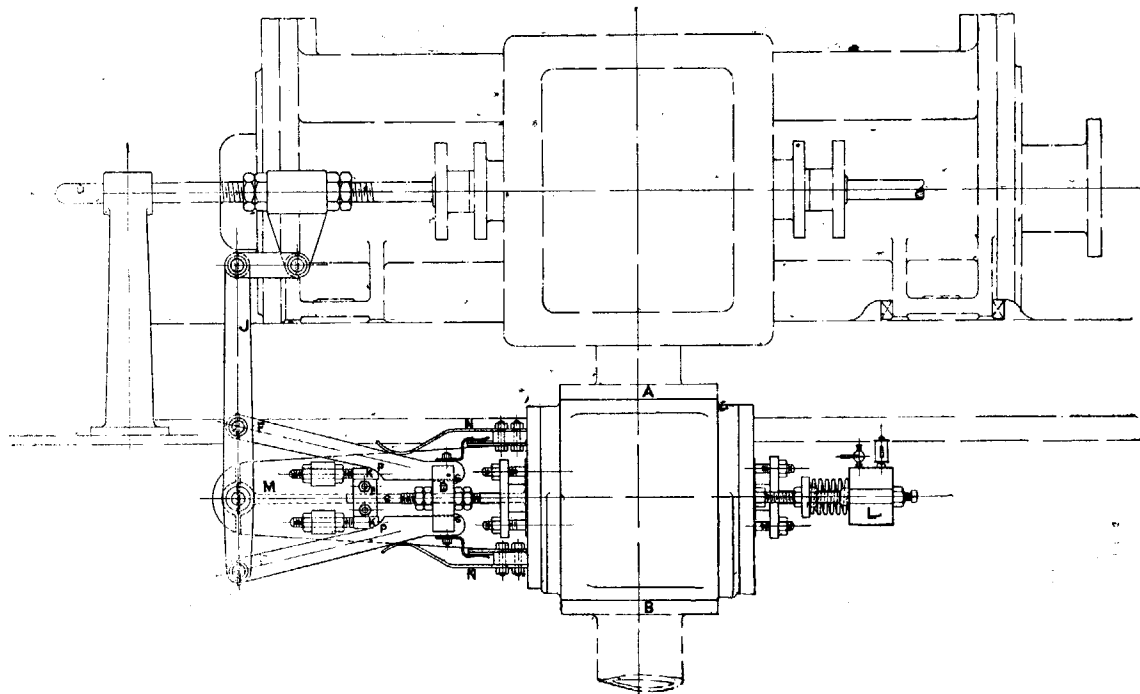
a. — El aparato colocado debajo de los cilindros.
